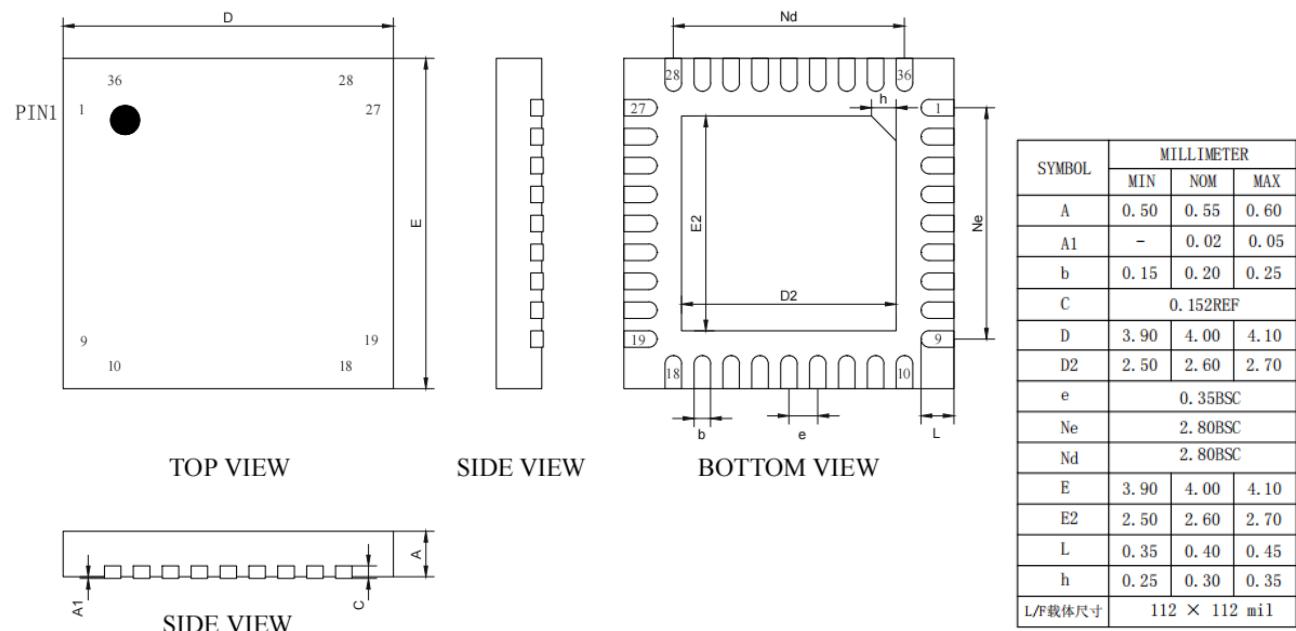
QFN36 (4*4*0.55-P0.35) 封装外形尺寸
